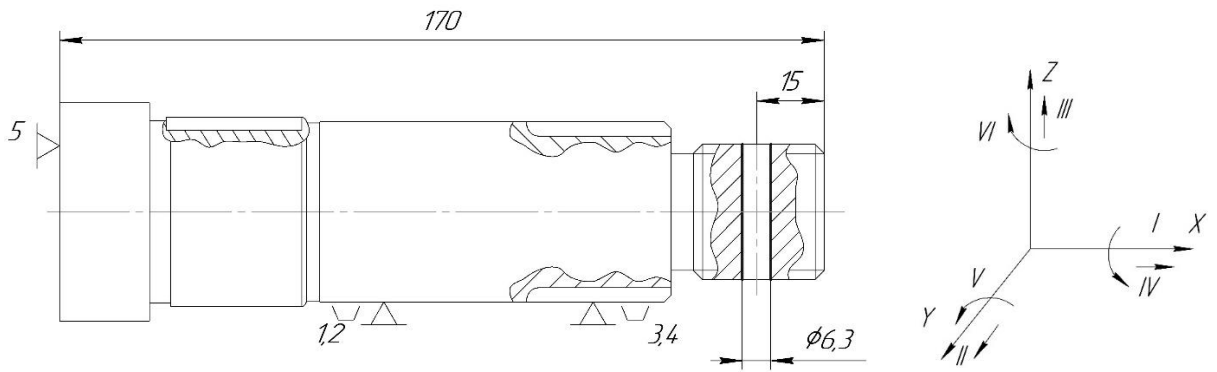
Схема базування та закріплення заготовки на операції
